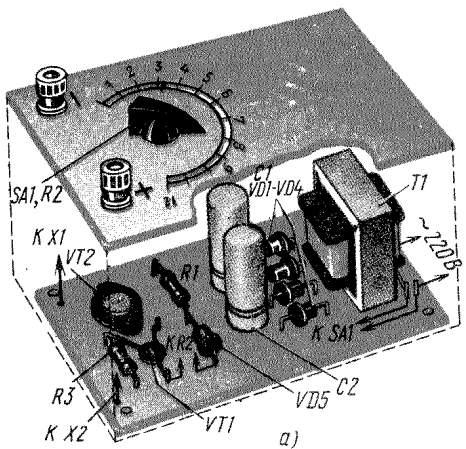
Конструкция сетевого блока питания и схема соединения деталей на монтажной плате
